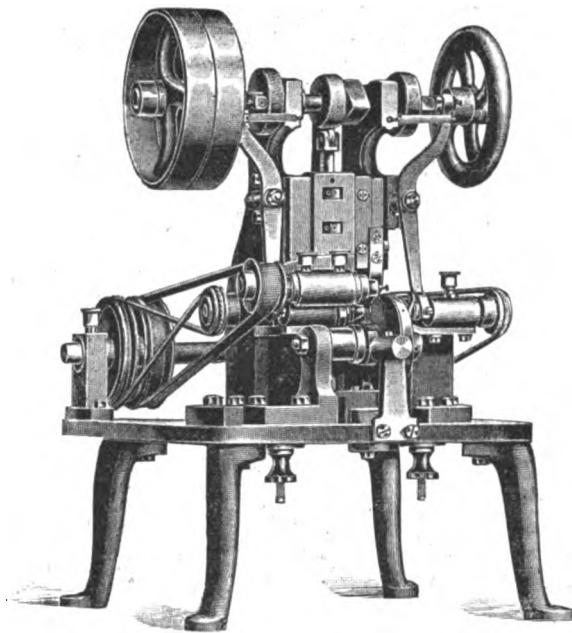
Maschine zum Einfräsen der Schlitz und Bohren der Löcher für die Finierstifte.
